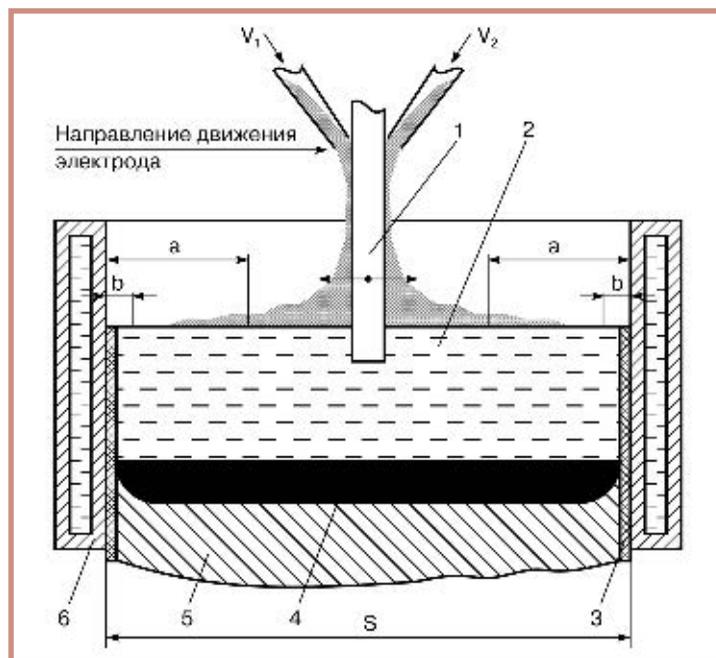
Схема процесса электрошлаковой наплавки: 1 — электрод неплавящийся; 2 — шлаковая ванна; 3 — шлаковая корка; 4 — металлическая ванна; 5 — заготовка било; 6 — кристаллизатор; V_1 , V_2 — подача порошкового присадочного материала
